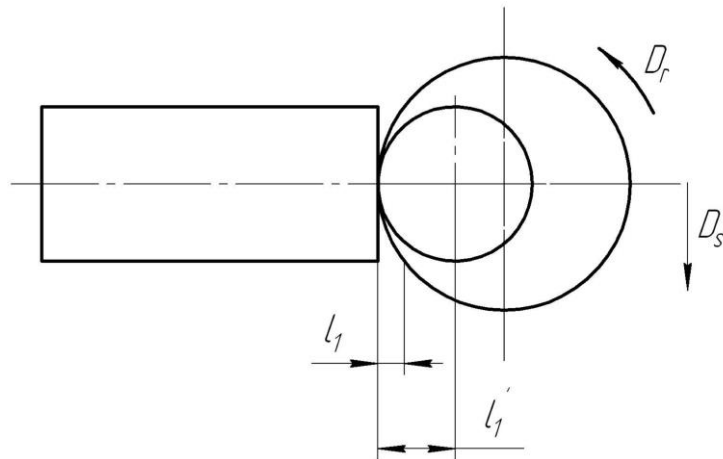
Схема фрезерования поверхности торцевой фрезой с различными диаметрами и изменением размера врезания
